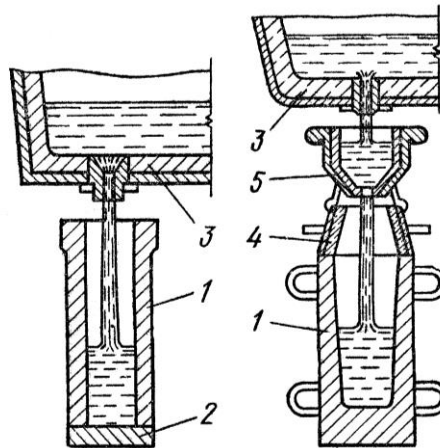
Схема разливки сверху: 1 — изложница; 2 — поддон;
